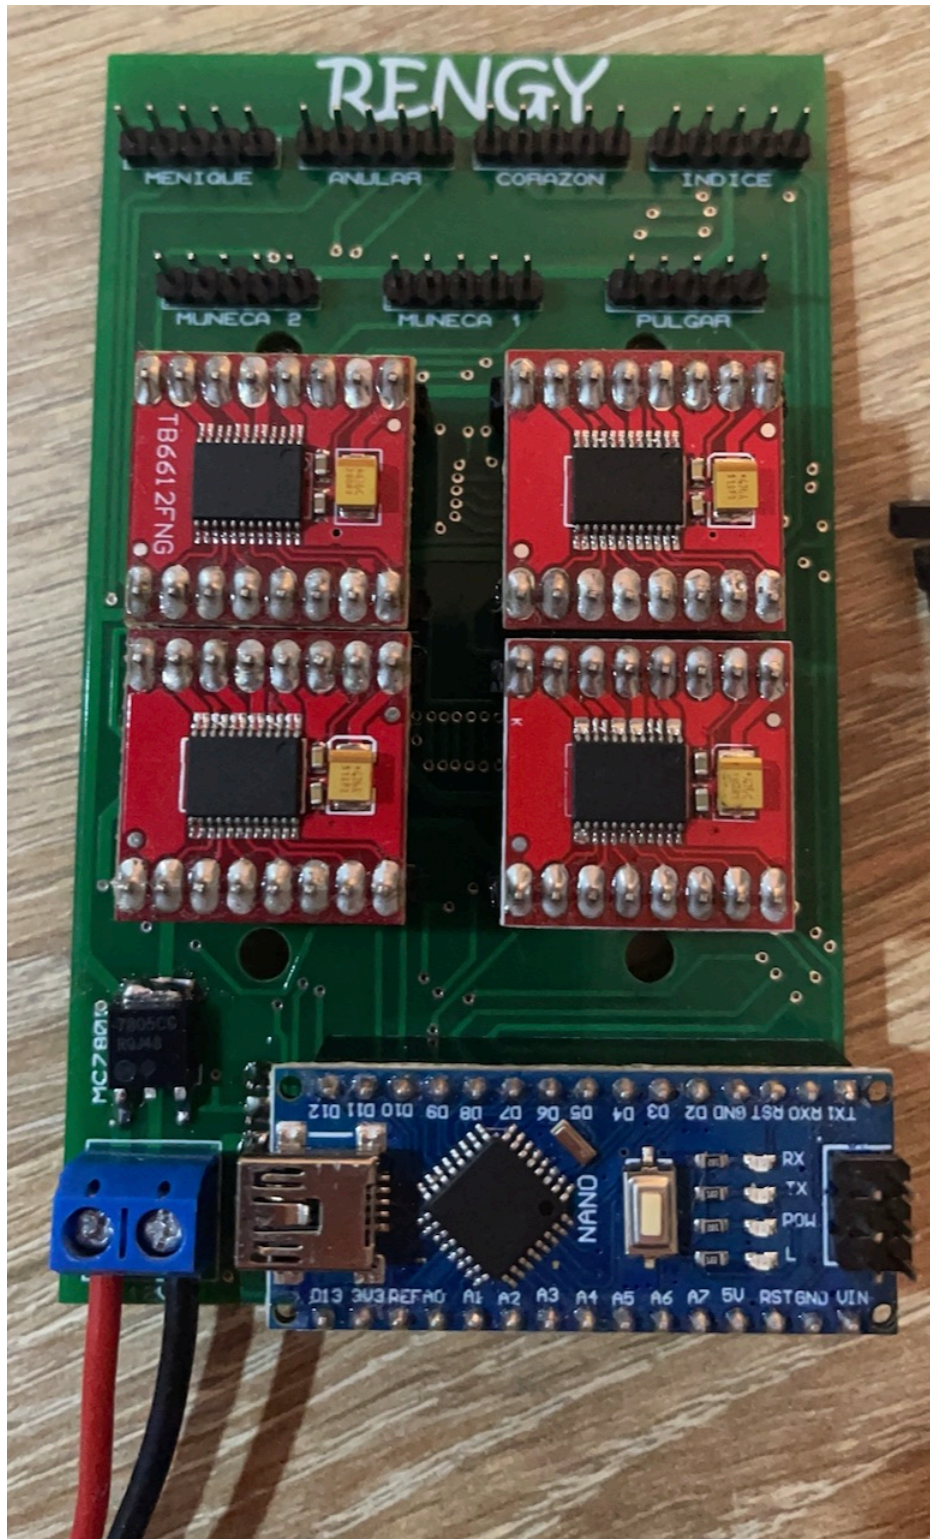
Segundo diseño con componentes soldados (Vista frontal).
